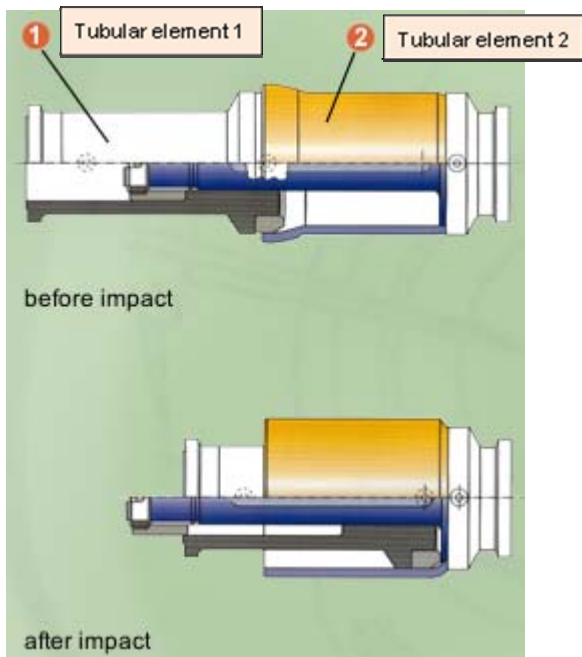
드뤄기어 조합체(Drawgear assembly)
